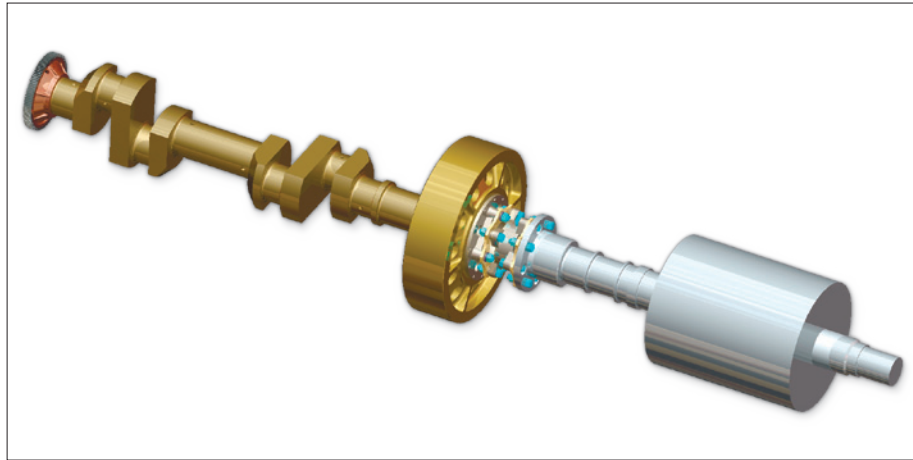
Общий вид валопровода поршневой компрессорной установки
